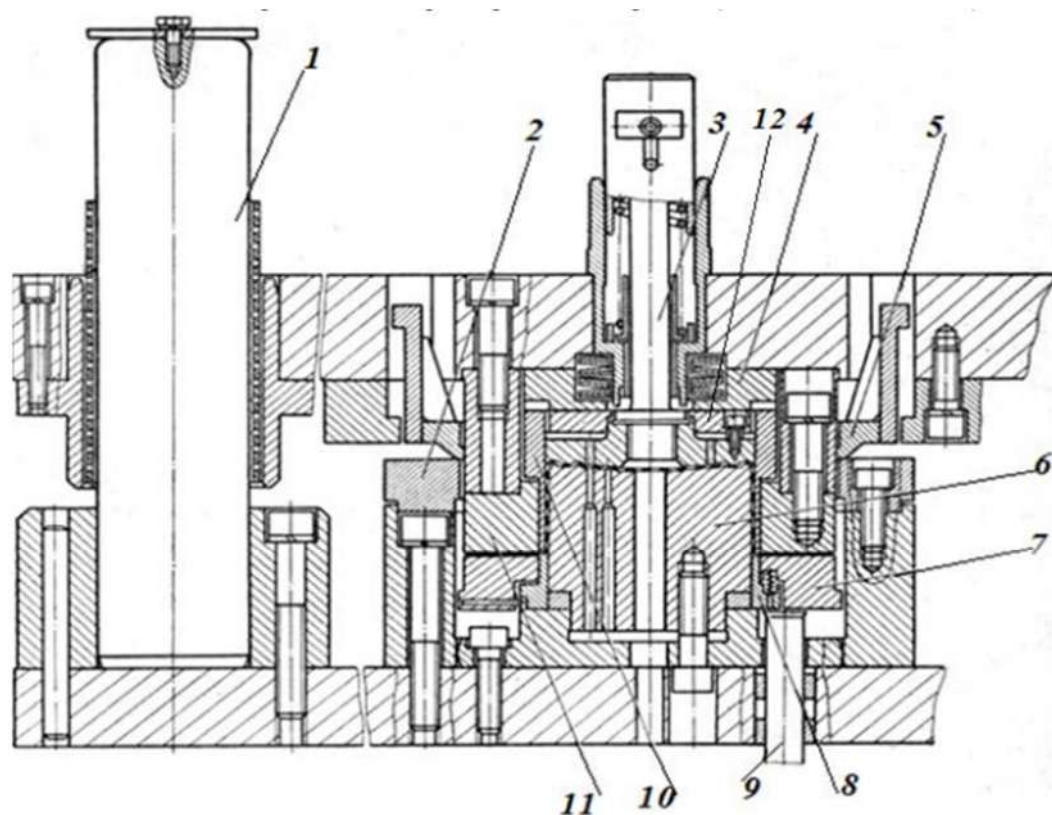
Комбінований штамп для глибокої витяжки жерстяних банок: 1 - пакет штампа з направляючими колонками; 2 - ріжуче кільце;
